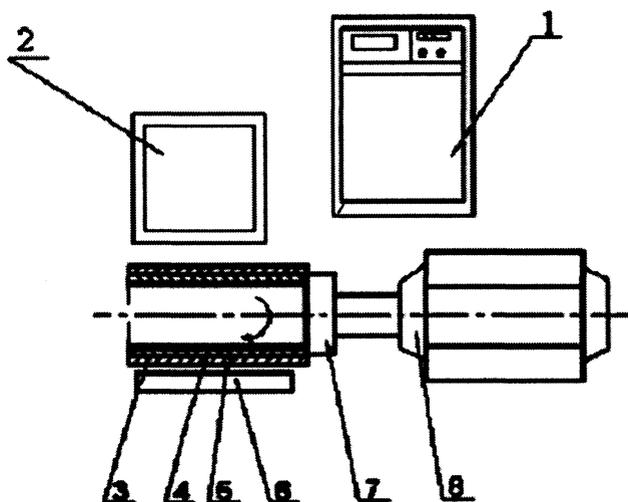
Схема установки с совмещенным плавлением шихты и подогревом стальной основы: 1 – высокочастотный генератор; 2 – вторичный трансформатор; 3 – стальная заготовка; 4 – наплавленный слой; 5 – флюс; 6 – индуктор; 7 – устройство крепления заготовки; 8 – привод вращения заготовки
